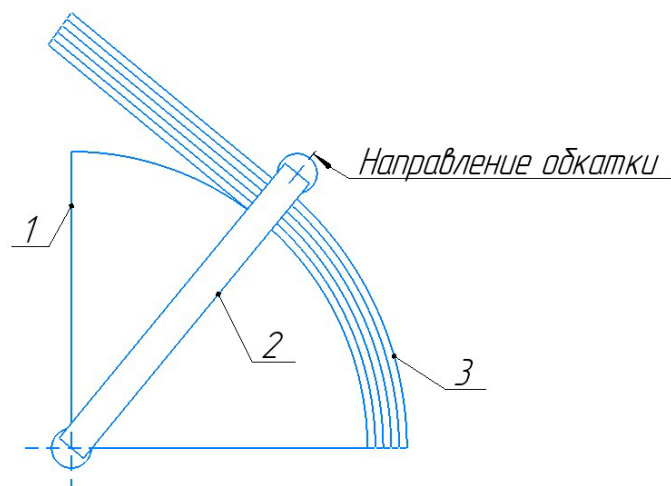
Принципиальная схема формирования полюсной катушки путем обкатки с использованием пневмомускул: 1 – шаблон для обкатки; 2 – пневмомускул; 3 – формируемая заготовка
